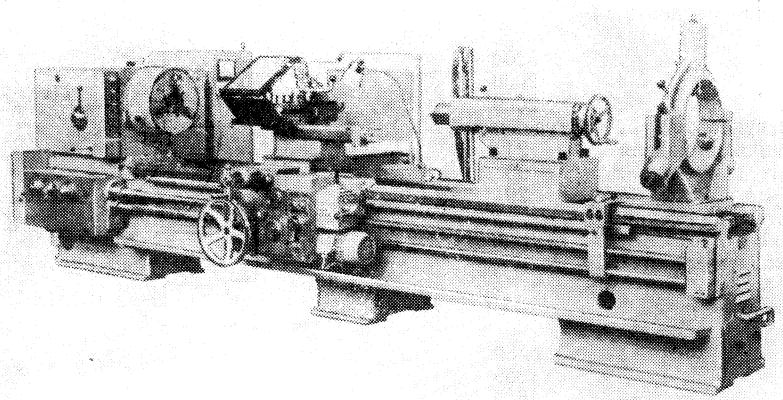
Общий вид токарно-винторезного станка мод. 16К40
